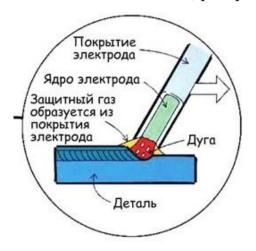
Дуговая сварка плавящимся электродом
